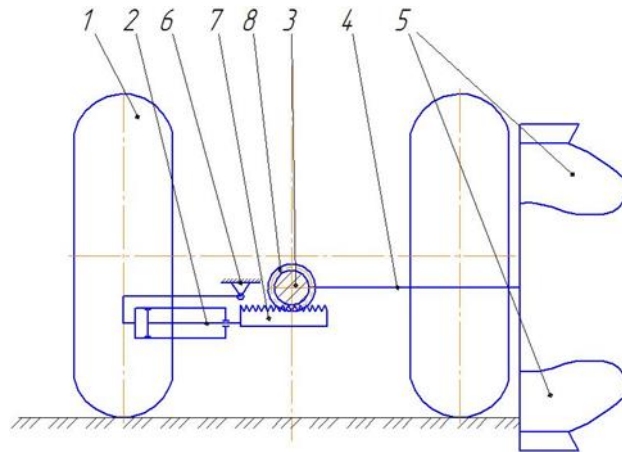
Механізм повороту плуга фірми «GregoireBesson»: 1 –тракторне колесо; 2 – гідроциліндр; 3 – рама; 4 – рама кріплення корпусу плуга; 5 – корпус плуга; 7 – рейка; 6 – тракторна підвіска; 8 – шестерня
